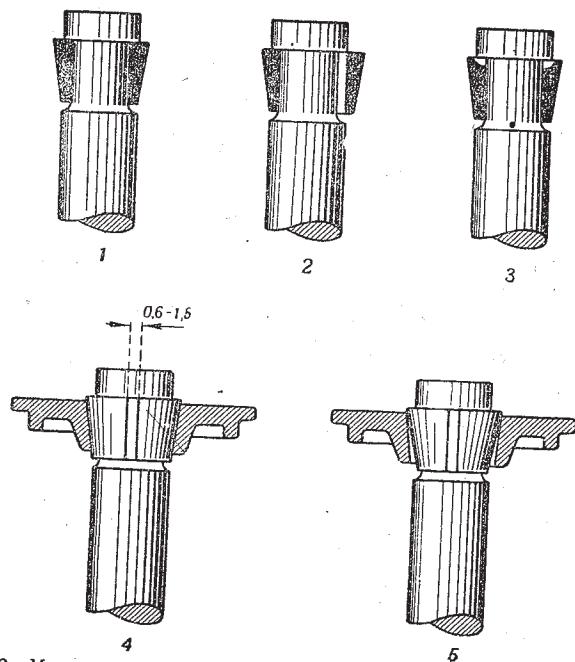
Монтаж замка и упорной шайбы клапанной пружины
